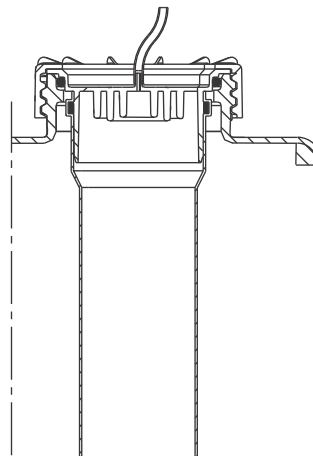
Schraubdeckel mit Schlauch und Staudruckrohr DN 100
